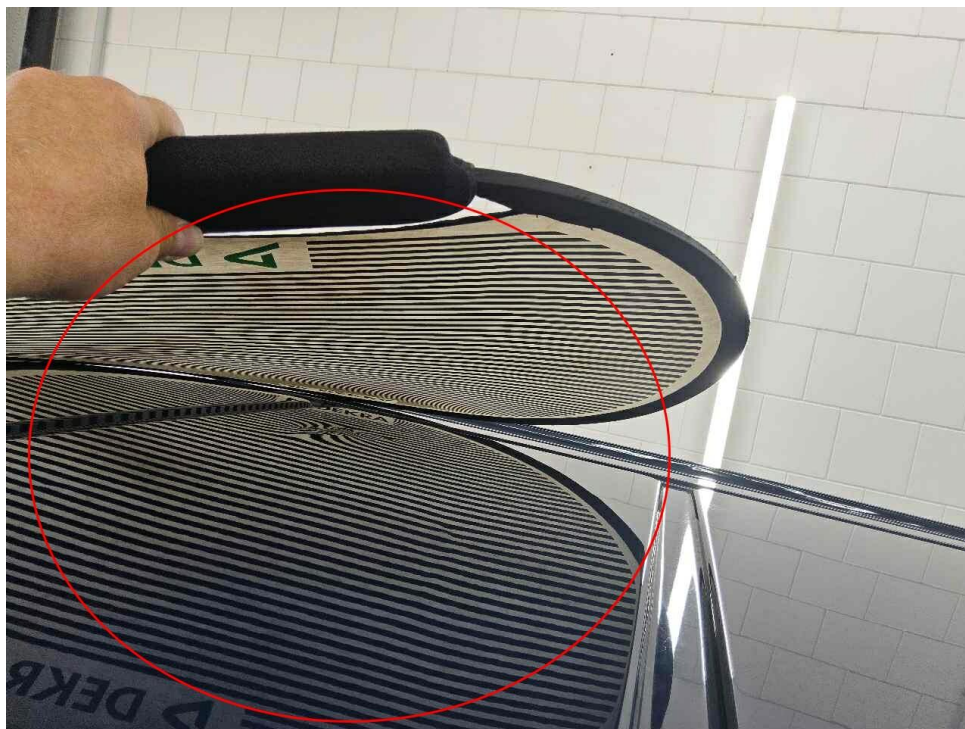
Dach, mehrfach eingedellt, instandsetzen und lackieren mit Lackaufbau
